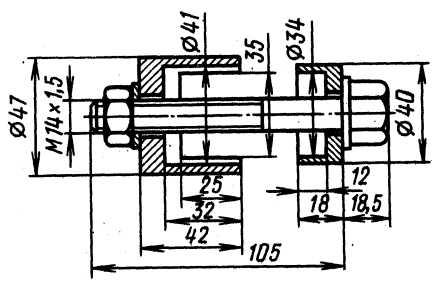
Приспособление для перепрессовки резинометаллических шарниров верхнего рычага передней подвески автомобиля «Жигули»
